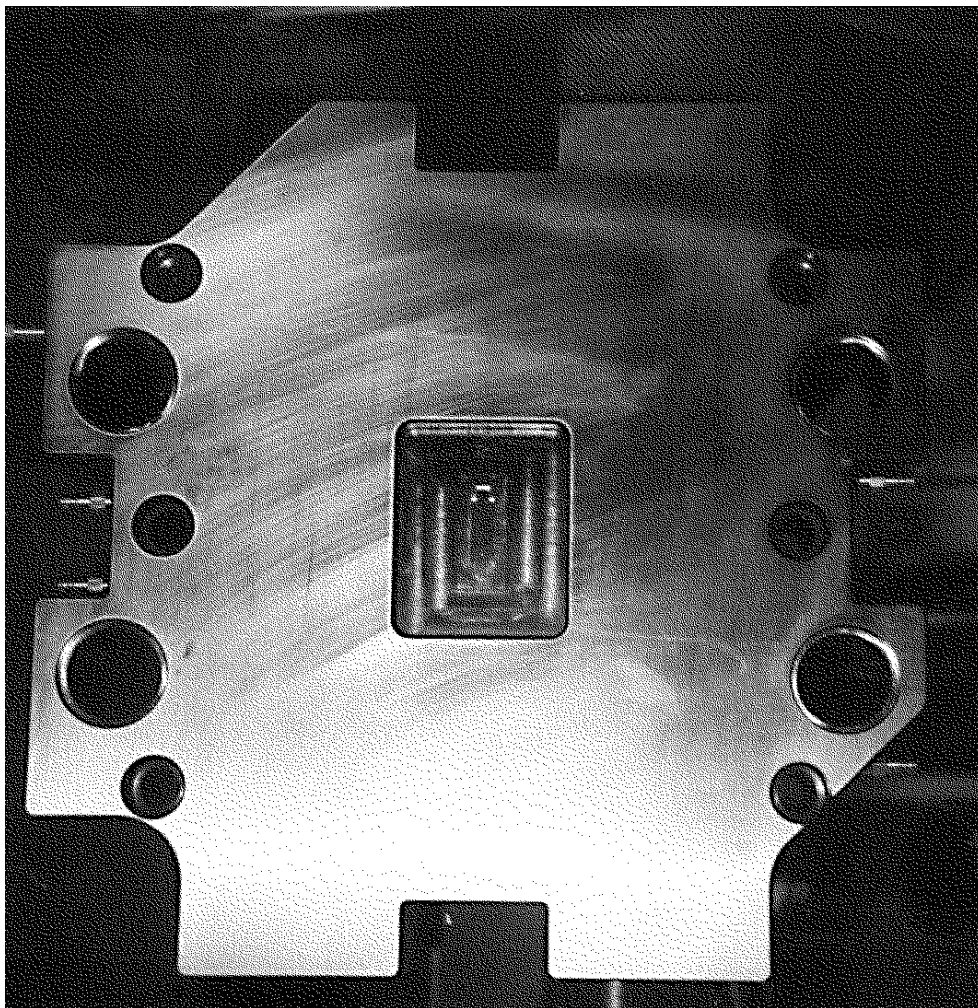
Kleine Kavität des Heißprägewerkzeuges [Mün]
